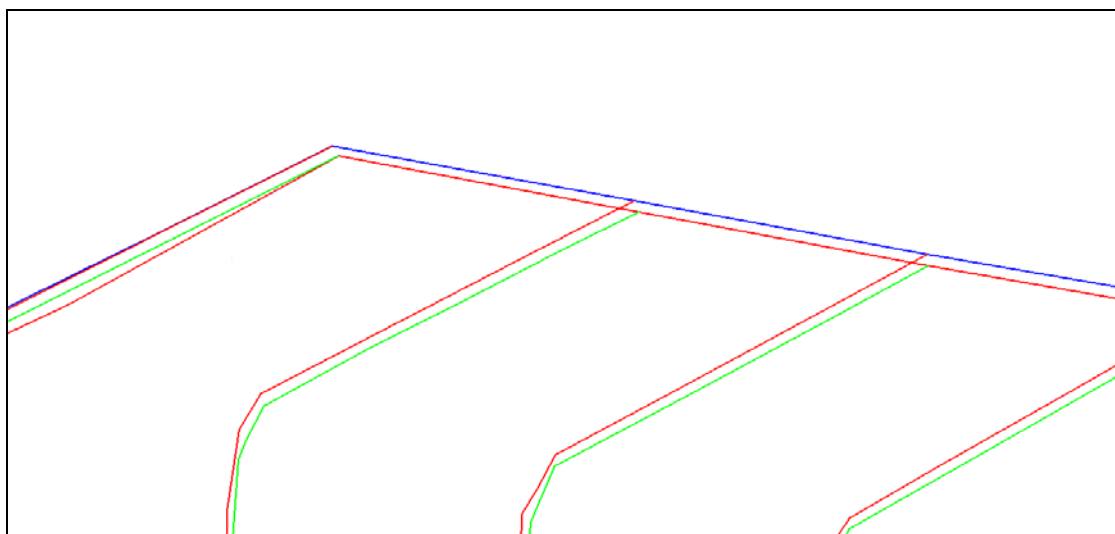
Πλάγια όψη, πλωραίο τμήμα. [AutoCAD Drawing]
